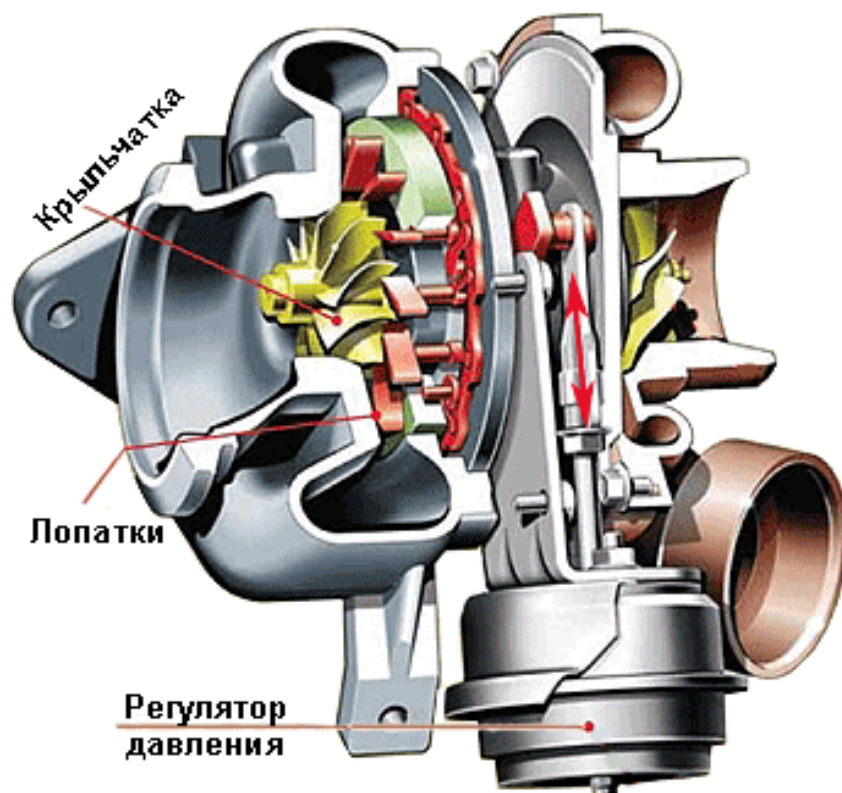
Общий вид турбокомпрессора с поворотом лопаток соплового аппарата турбины
